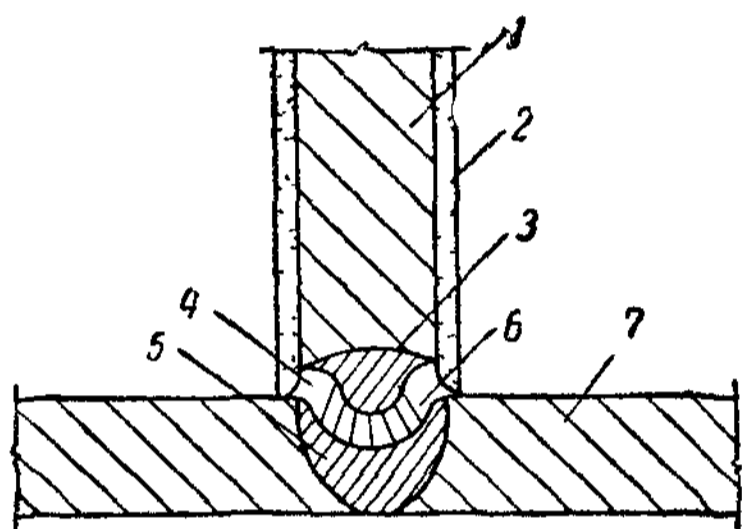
Схема сварки с глубоким проплавлением
